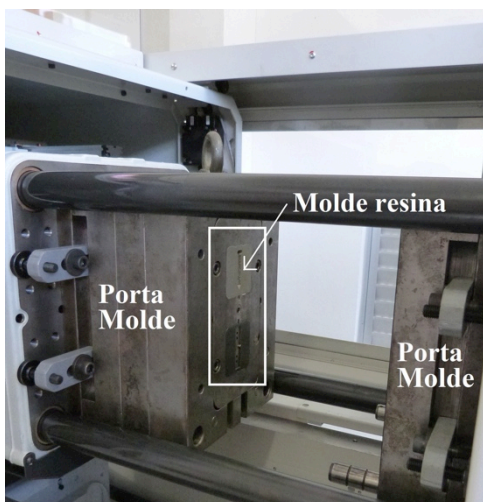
Molde em resina montado no porta molde na máquina injetora.
